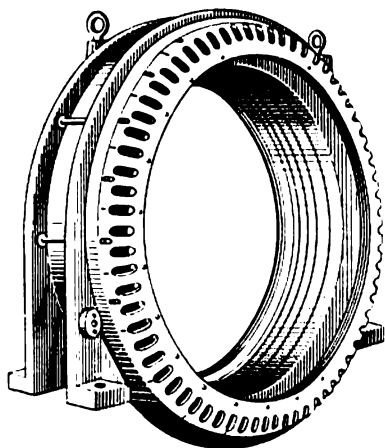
Vue extérieure du stator d'un alternateur synchrone
